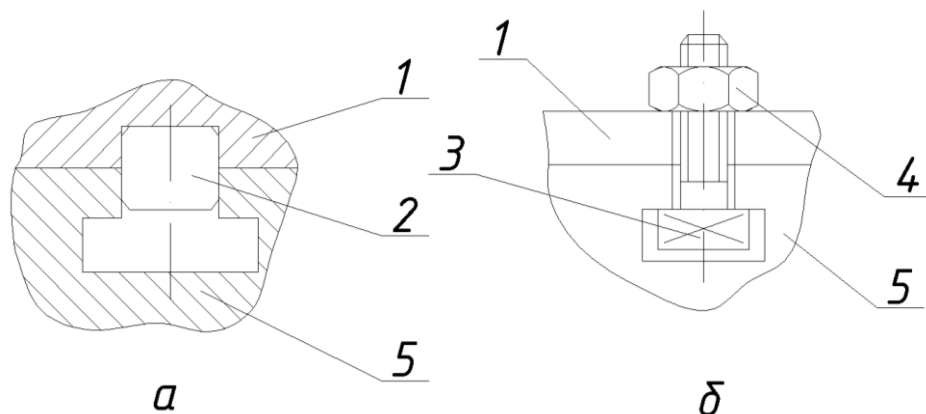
Способи точного встановлення та кріплення пристрою: 1 – плита; 2 – шпонка; 3 – болт; 4 – гайка; 5 – стіл.
